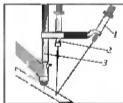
Точечный лазер на сварочной головке:
